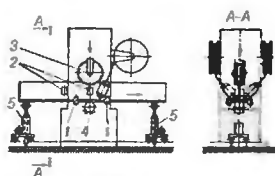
Схема верстата для зварювання балок таврового профілю: 1, 2 — роликi для центрування елементів тавра; 3 — натискний ролик; 4 — привідний ролик; 5 — роликi опорних візків
